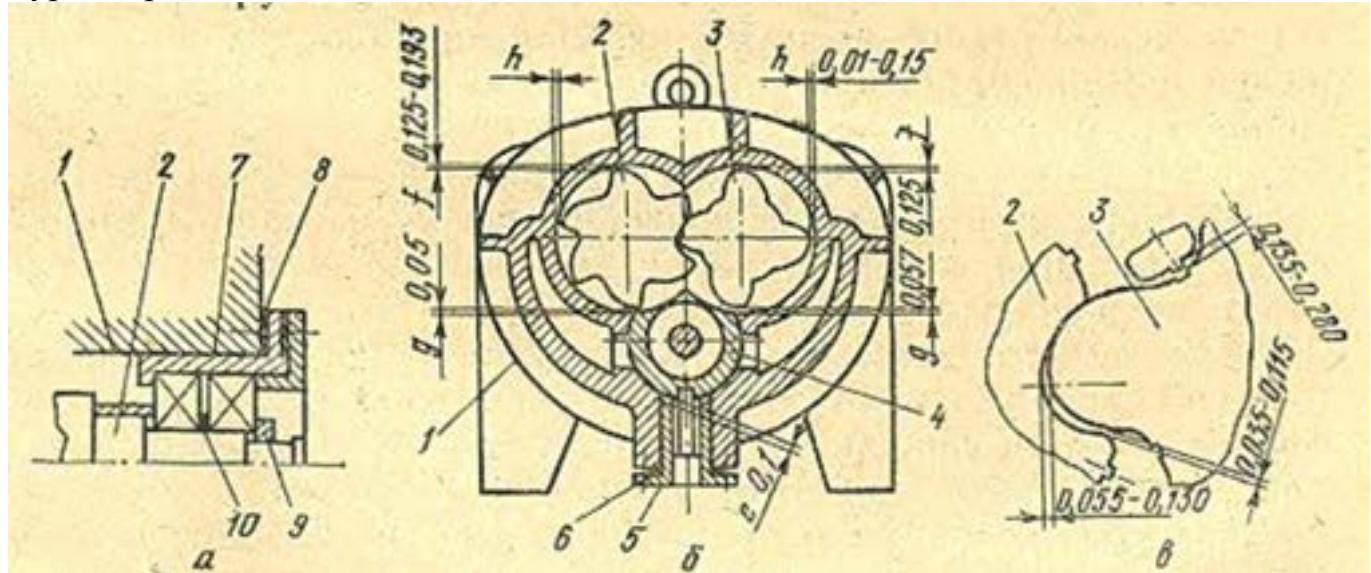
Схема регулировки и измерения зазоров в подшипниках качения (а) радиальных (б) и профильных (в) винтовых компрессорах:
